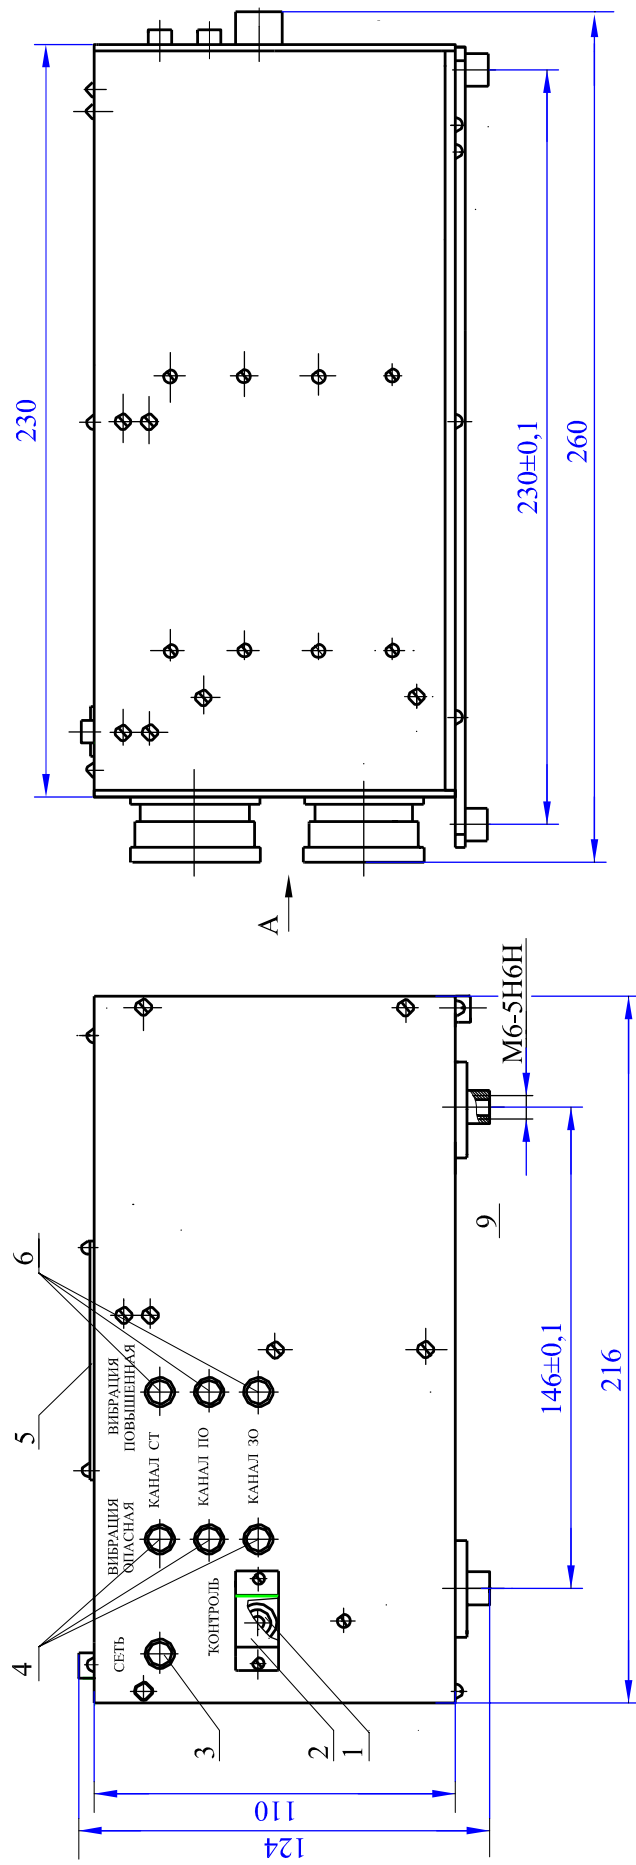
(1 из 2) - Габаритно - установочные размеры блока БЭ - 38 - 14М
